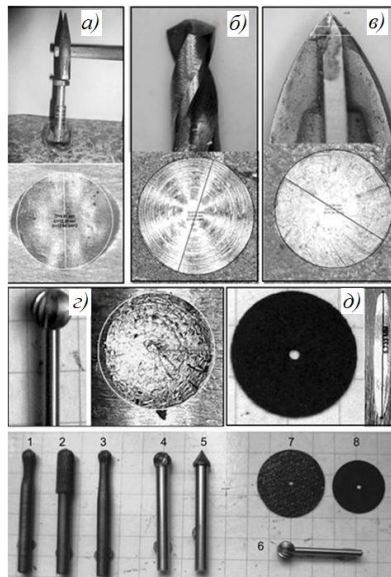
Инструменты и вид лунок, образованных: а – ударным способом, путем вдавливания шарика; б - высверливанием при помощи сверла при  $\varphi = 118^\circ$ ; в – выскабливанием сверлом для керамики; г – фрезерованием шарообразной мини фрезой диаметром 7,8 мм; е – надрезом мини болгаркой. Инструменты: 1-3 – шарошки, 4-5 – фрезы, 6 – шарообразная мини фреза, 7-8 – мини болгарки диаметром 22,5 и 24 мм
